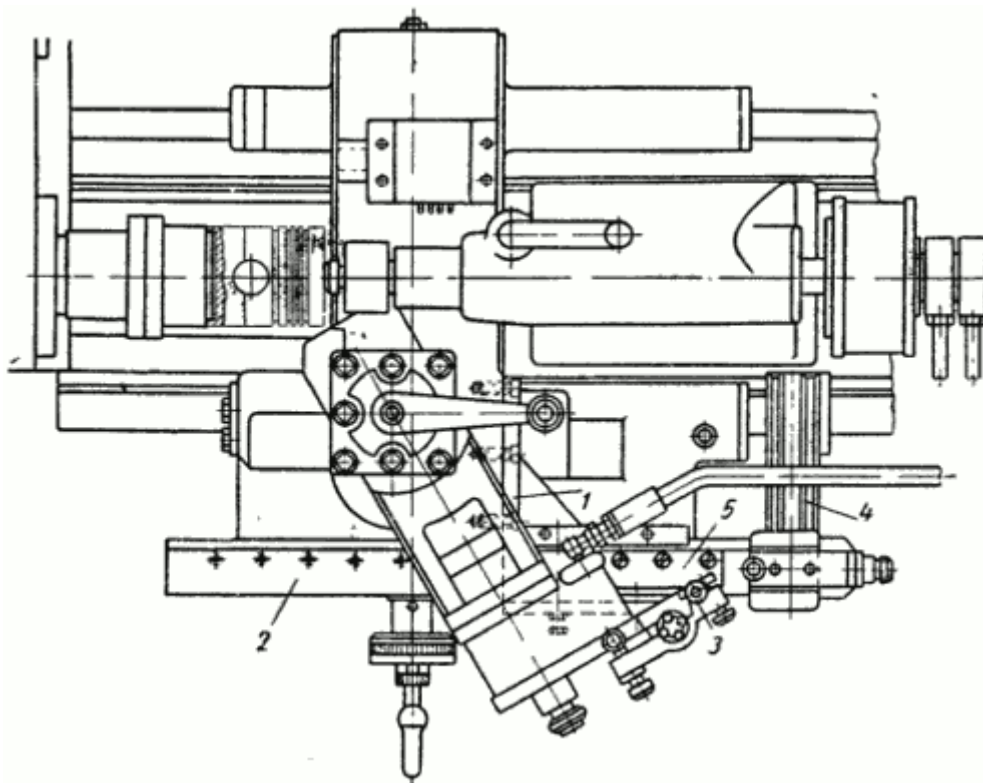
Установка гидроконтрольного суппорта ГС-1 на токарно-винторезном станке
